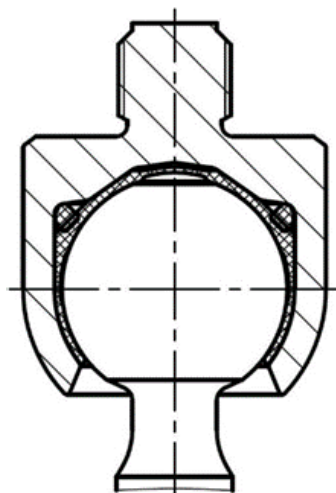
Вид сдеформированного (опрессованного) корпуса
